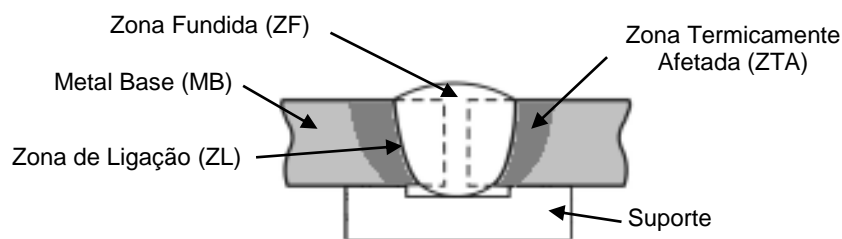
Posição do suporte junto com o cordão de solda (Marques e Modenesi, 2006).
